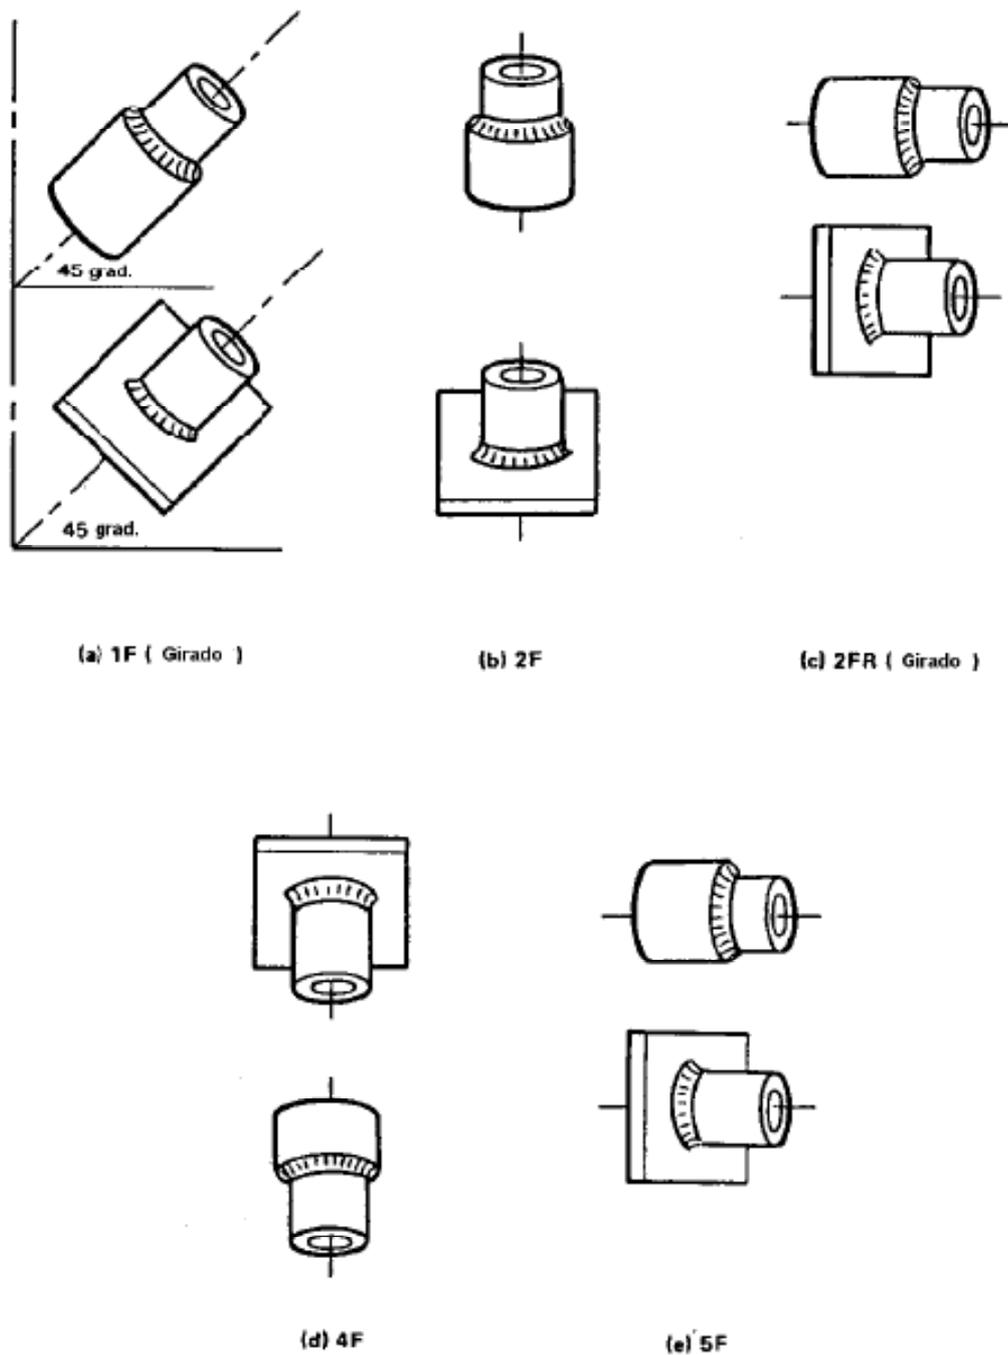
Posiciones de Prueba para Soldadura de Tubos a Filete; (a) Posición Plana, (b) Posición Horizontal, (c) Posición Horizontal Rotada, (d) Posición Sobre Cabeza, y; (e) Posición Múltiple
